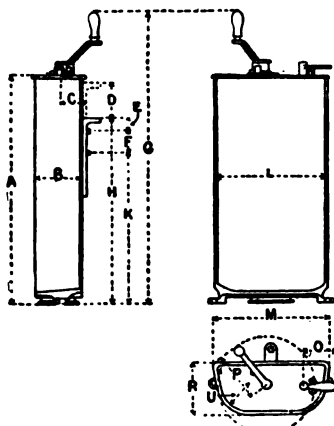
Dimensions des régulateurs de la General Electric Co.
